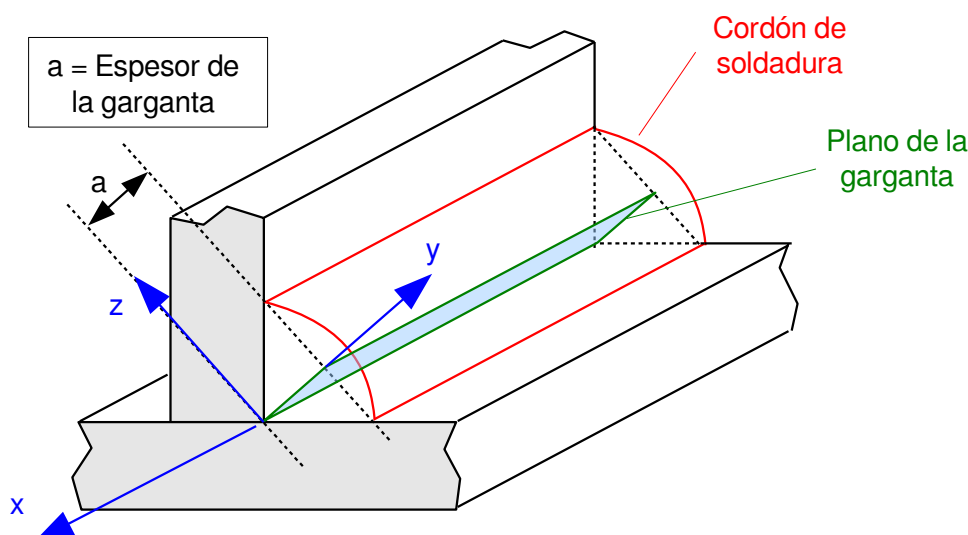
Cordón de soldadura entre dos placas.
